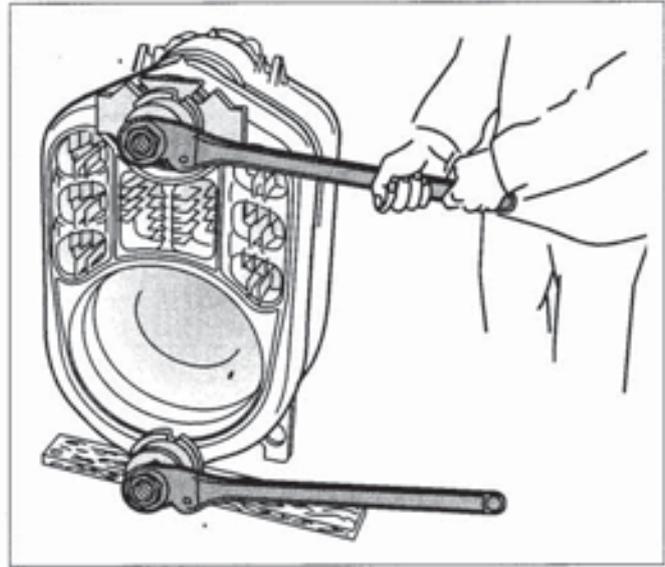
Sicheres Arbeiten mit dem Presswerkzeug
